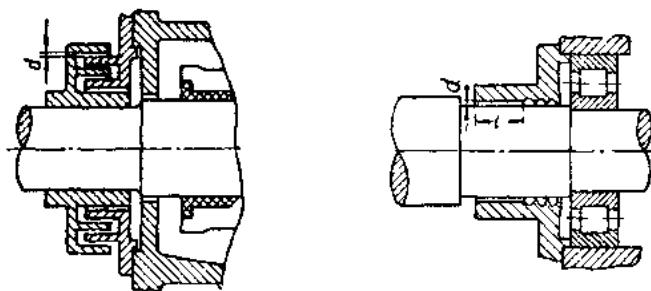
适合于电动机和发电机的滑动轴承,球轴承或滚柱轴承的迷宫式防爆密封装置
